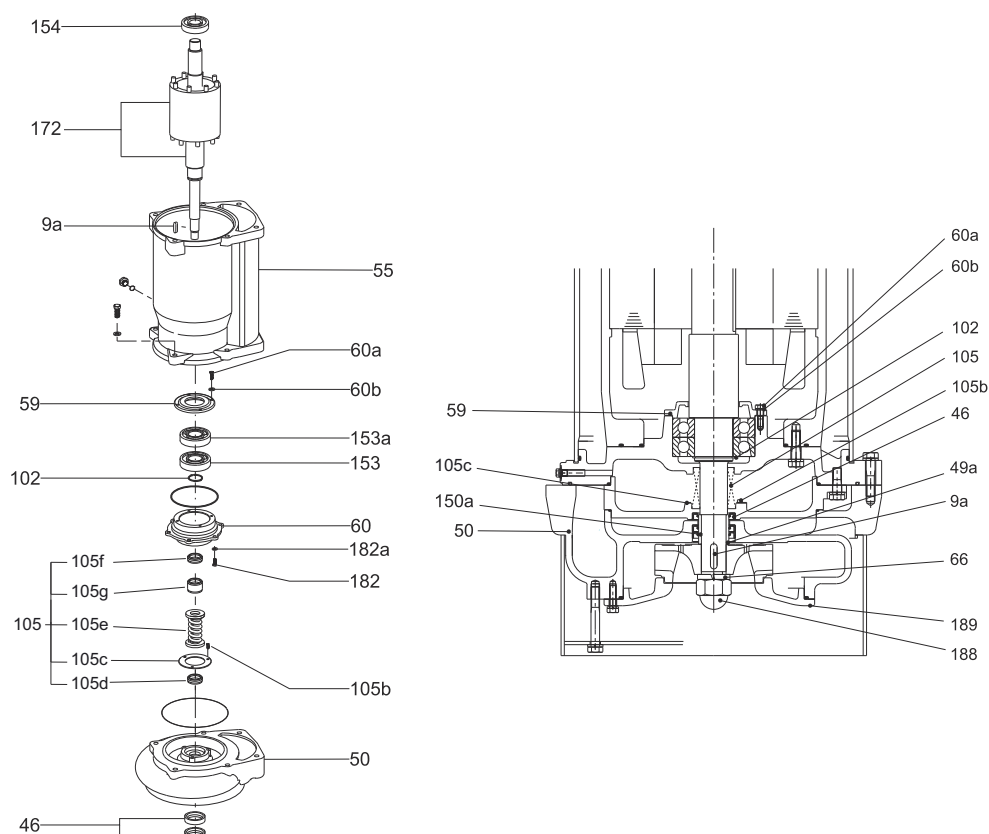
Демонтаж торцевого уплотнения и подшипников
